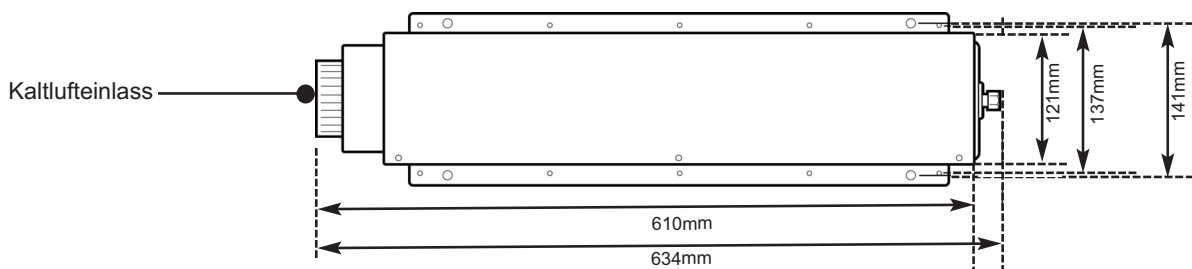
Interne Montage - Draufsicht - SH2201 oder SC2201
